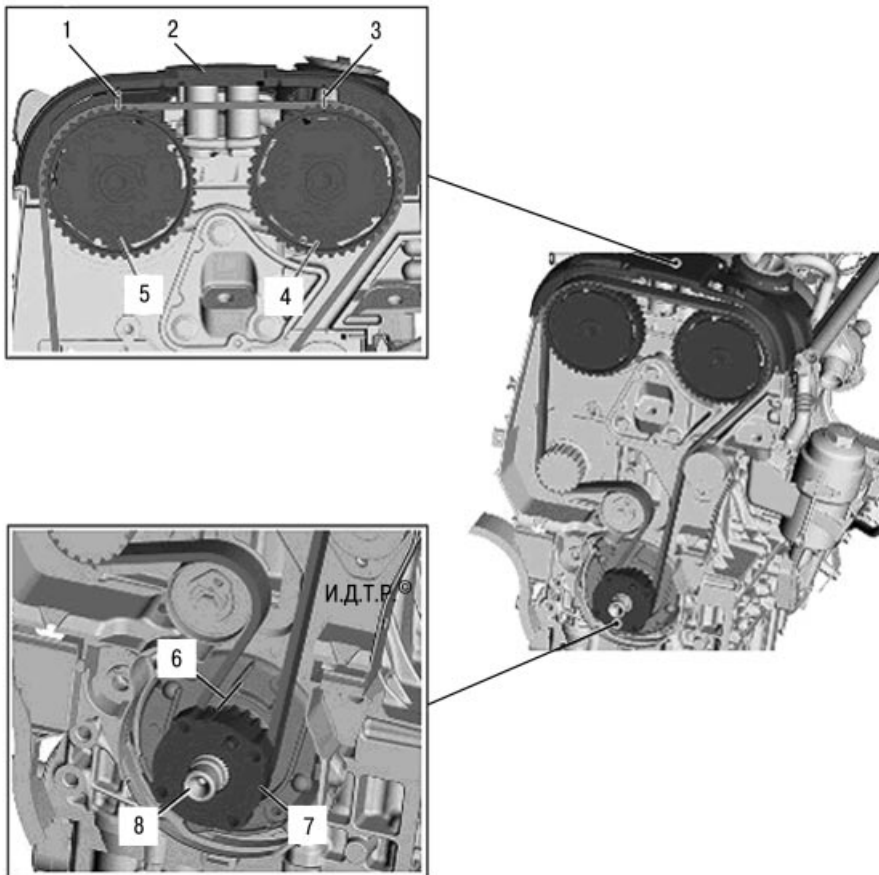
Установочные метки (фазы газораспределения): 1 – установочная метка шкива выпускного распределительного вала; 2 – крышка привода газораспределительного механизма с установочными метками; 3 – установочная метка шкива впускного распределительного вала; 4 – зубчатый шкив впускного распределительного вала; 5 – зубчатый шкив выпускного распределительного вала; 6 – установочная метка зубчатого шкива привода газораспределительного механизма на коленчатом валу; 7 – зубчатый шкив ремня привода газораспределительного механизма на коленчатом валу; 8 – коленчатый вал
